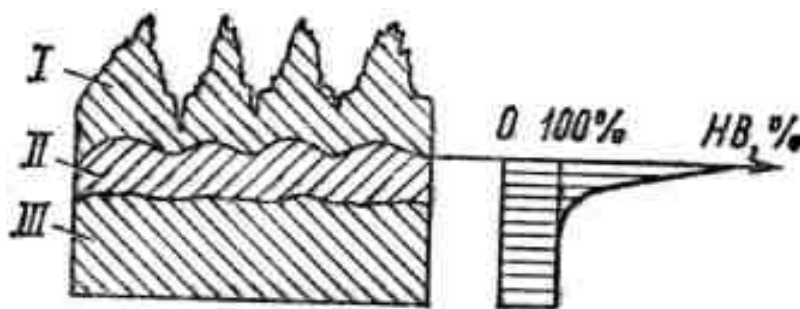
Поверхностный слой материала заготовки (а – строение, б – эпюра изменения твердости)
